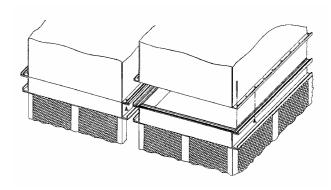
Accoppiamento sezione scambio/ventilante con sezione bacino
